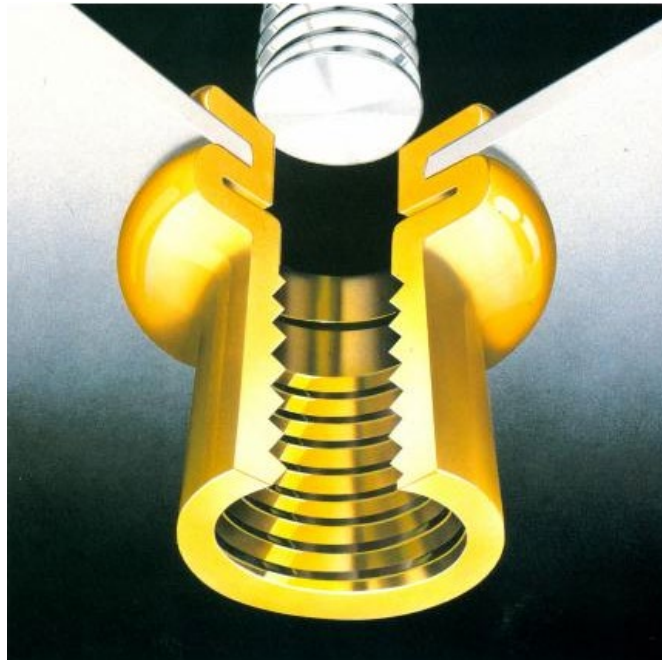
Ejemplo de pieza en corte con inserto roscado. [H-44]
